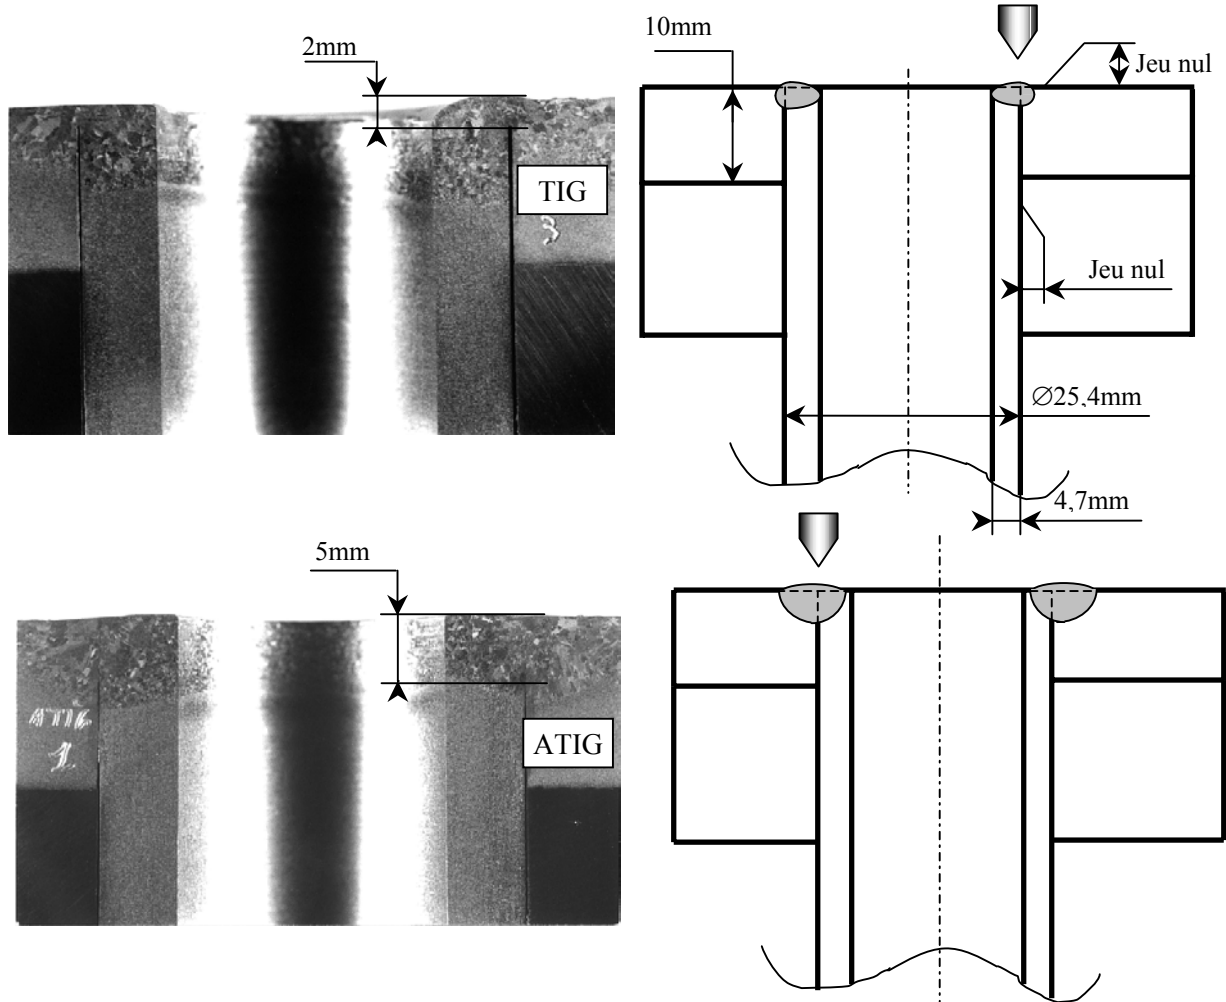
Soudure tube sur plaque automatique TIG - ATIG (courant pulsé 120/80A) (T40)
